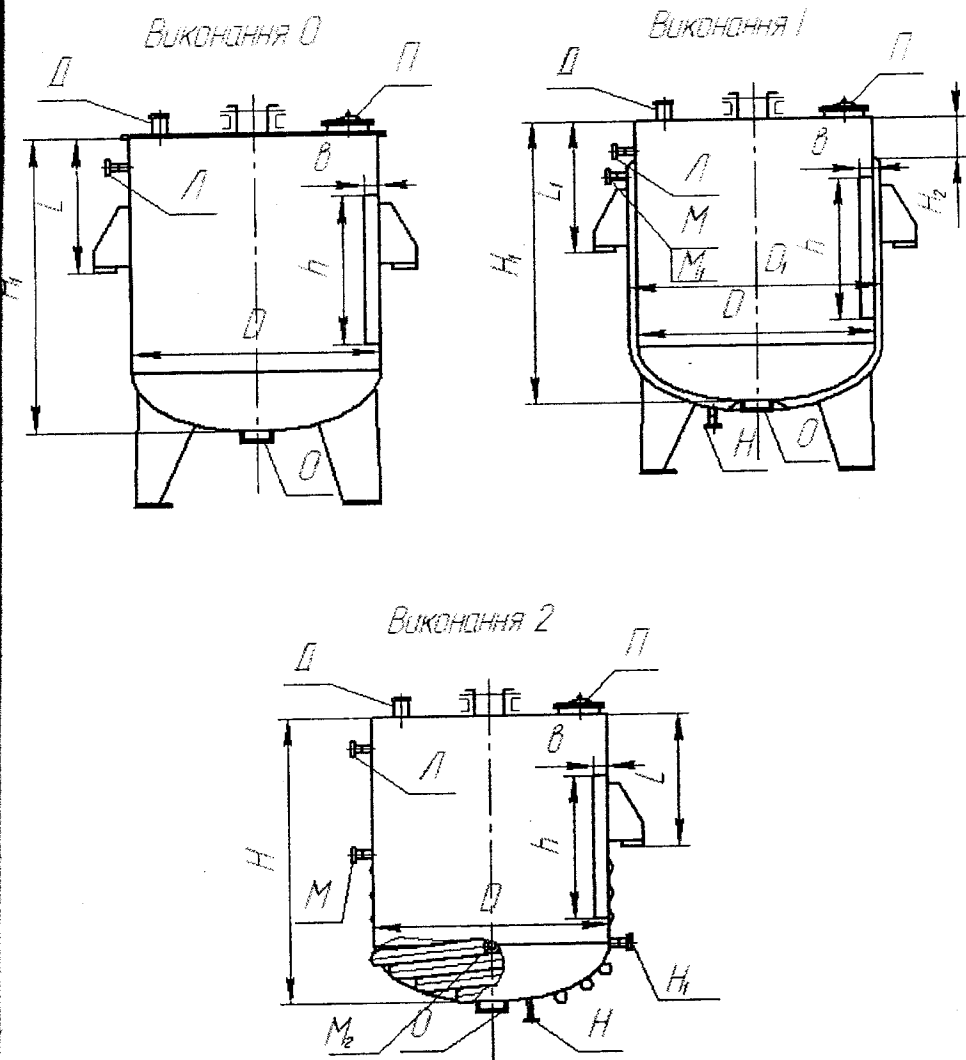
Корпуси типу 3 з приварною кришкою
